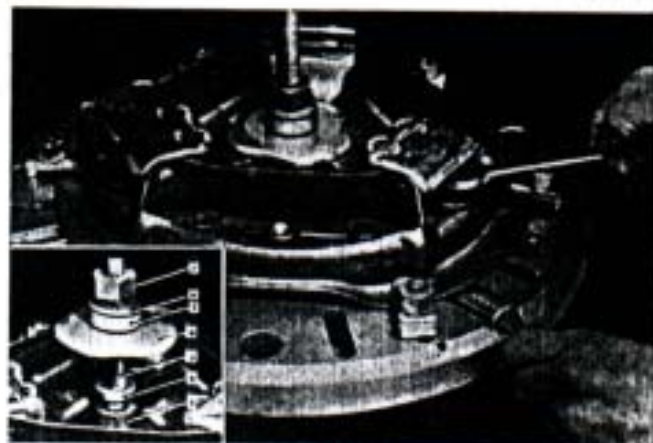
Ajustando el embrague "AUBURN" en el plato HS-64.
